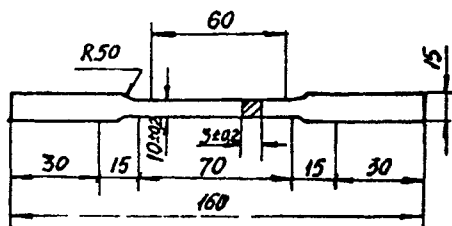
Форма і розміри зразка для лиття під тиском
